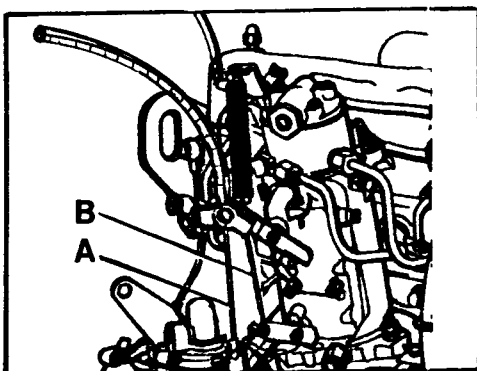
Desmontaje de los cables de acelerador y estrangulador
